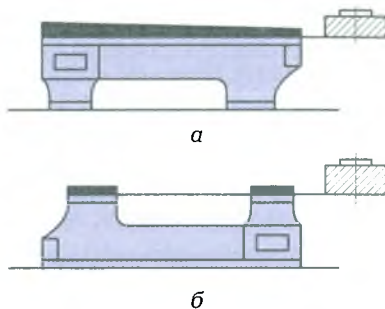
Схема последовательности обработки станины станка, обеспечивающая равномерность снимаемого слоя металла с поверхности ножек:
